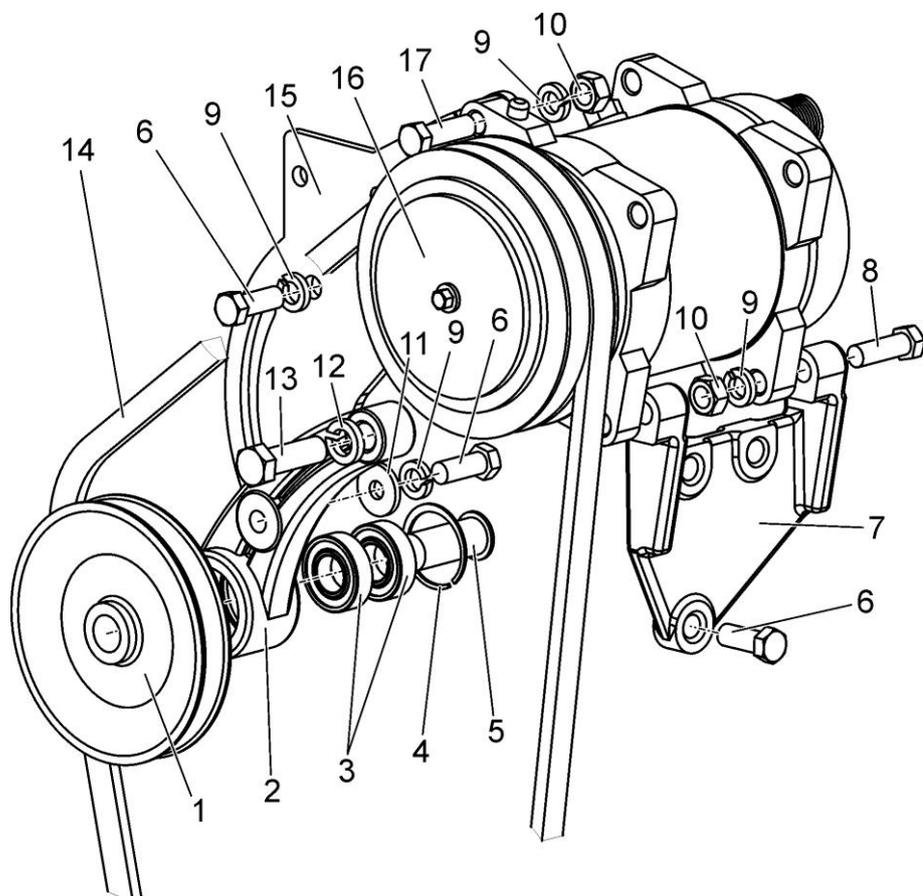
Компрессор кондиционера с приводом. Рычаг натяжной
